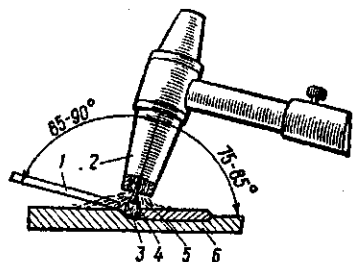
Расположение горелки и присадочного прутка при ручной аргонно-дуговой сварке:
